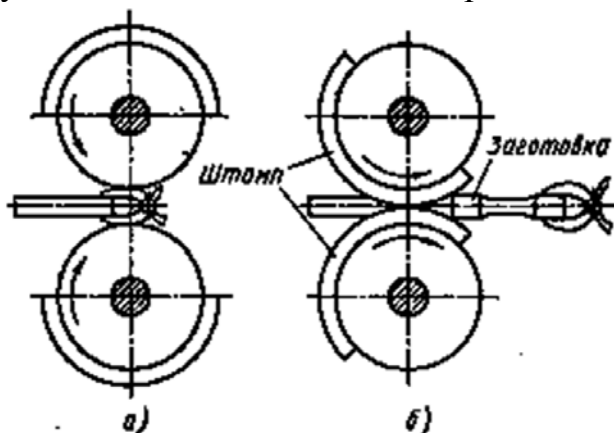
Схема вальцовки на ковочных вальцах: а – исходное положение; б – вальцовка
